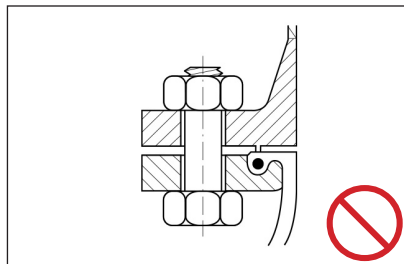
Zum Schutz des Gummis keine Flansche mit Nut und Feder benutzen, die das Gummi beschädigen können.
